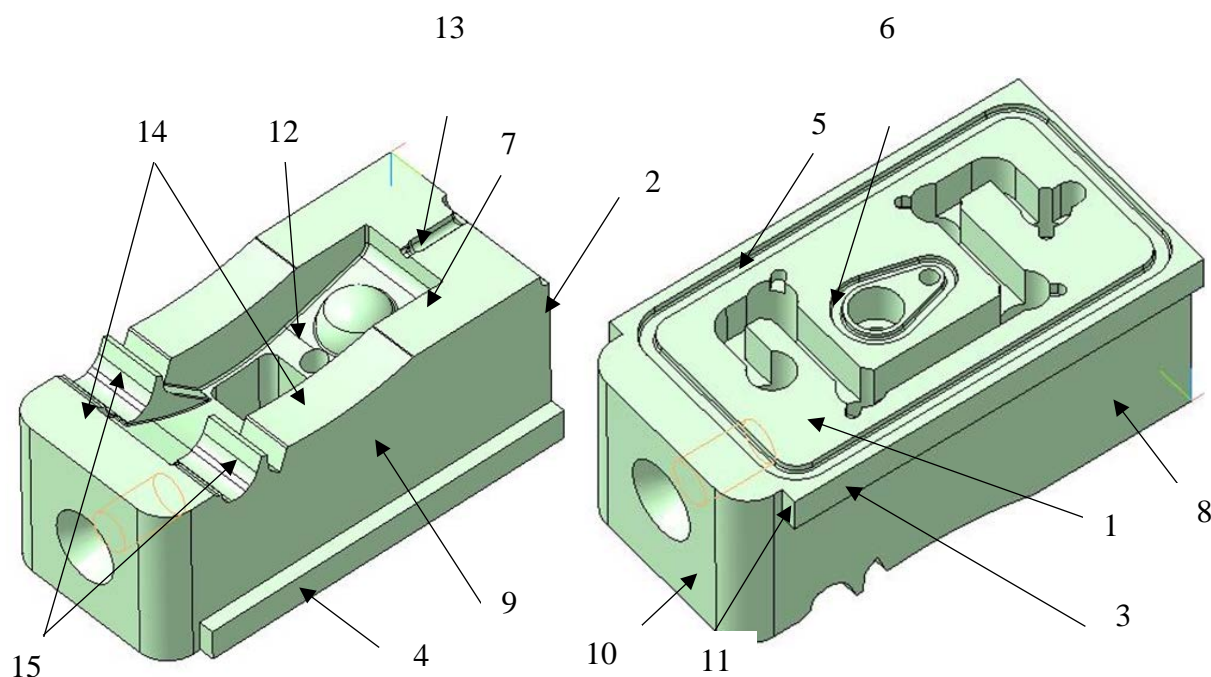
Обозначение поверхностей для обработки детали «Матрица»
